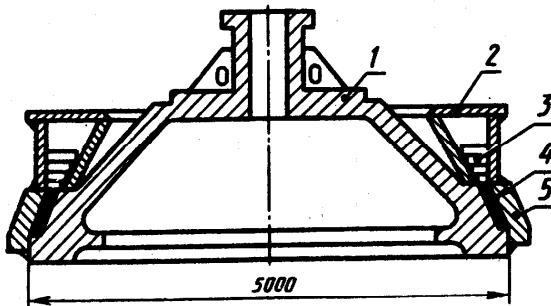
Схема наплавки композиционным сплавом контактной поверхности большого конуса
